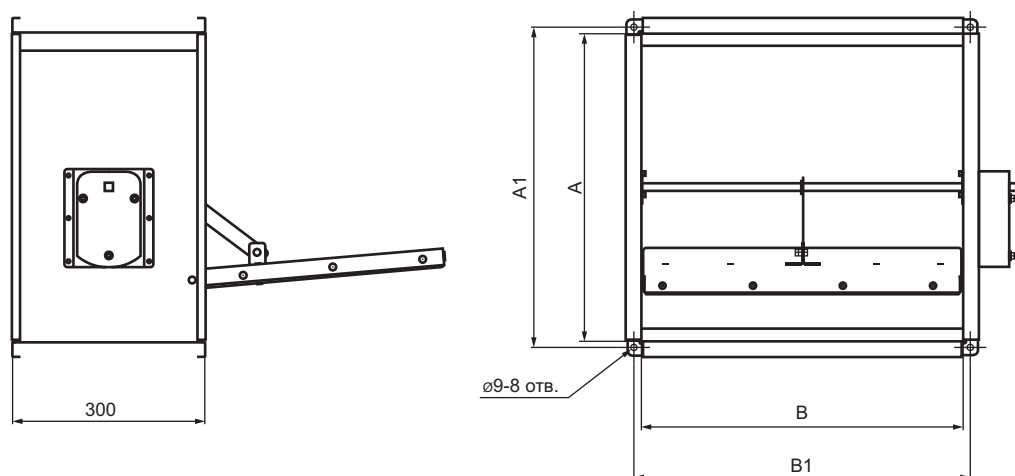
Габаритные и присоединительные размеры клапанов типа КВМ-Д с фланцевым соединением.
